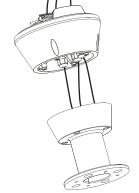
Führung der Kabel durch die Kabelverschraubungen
